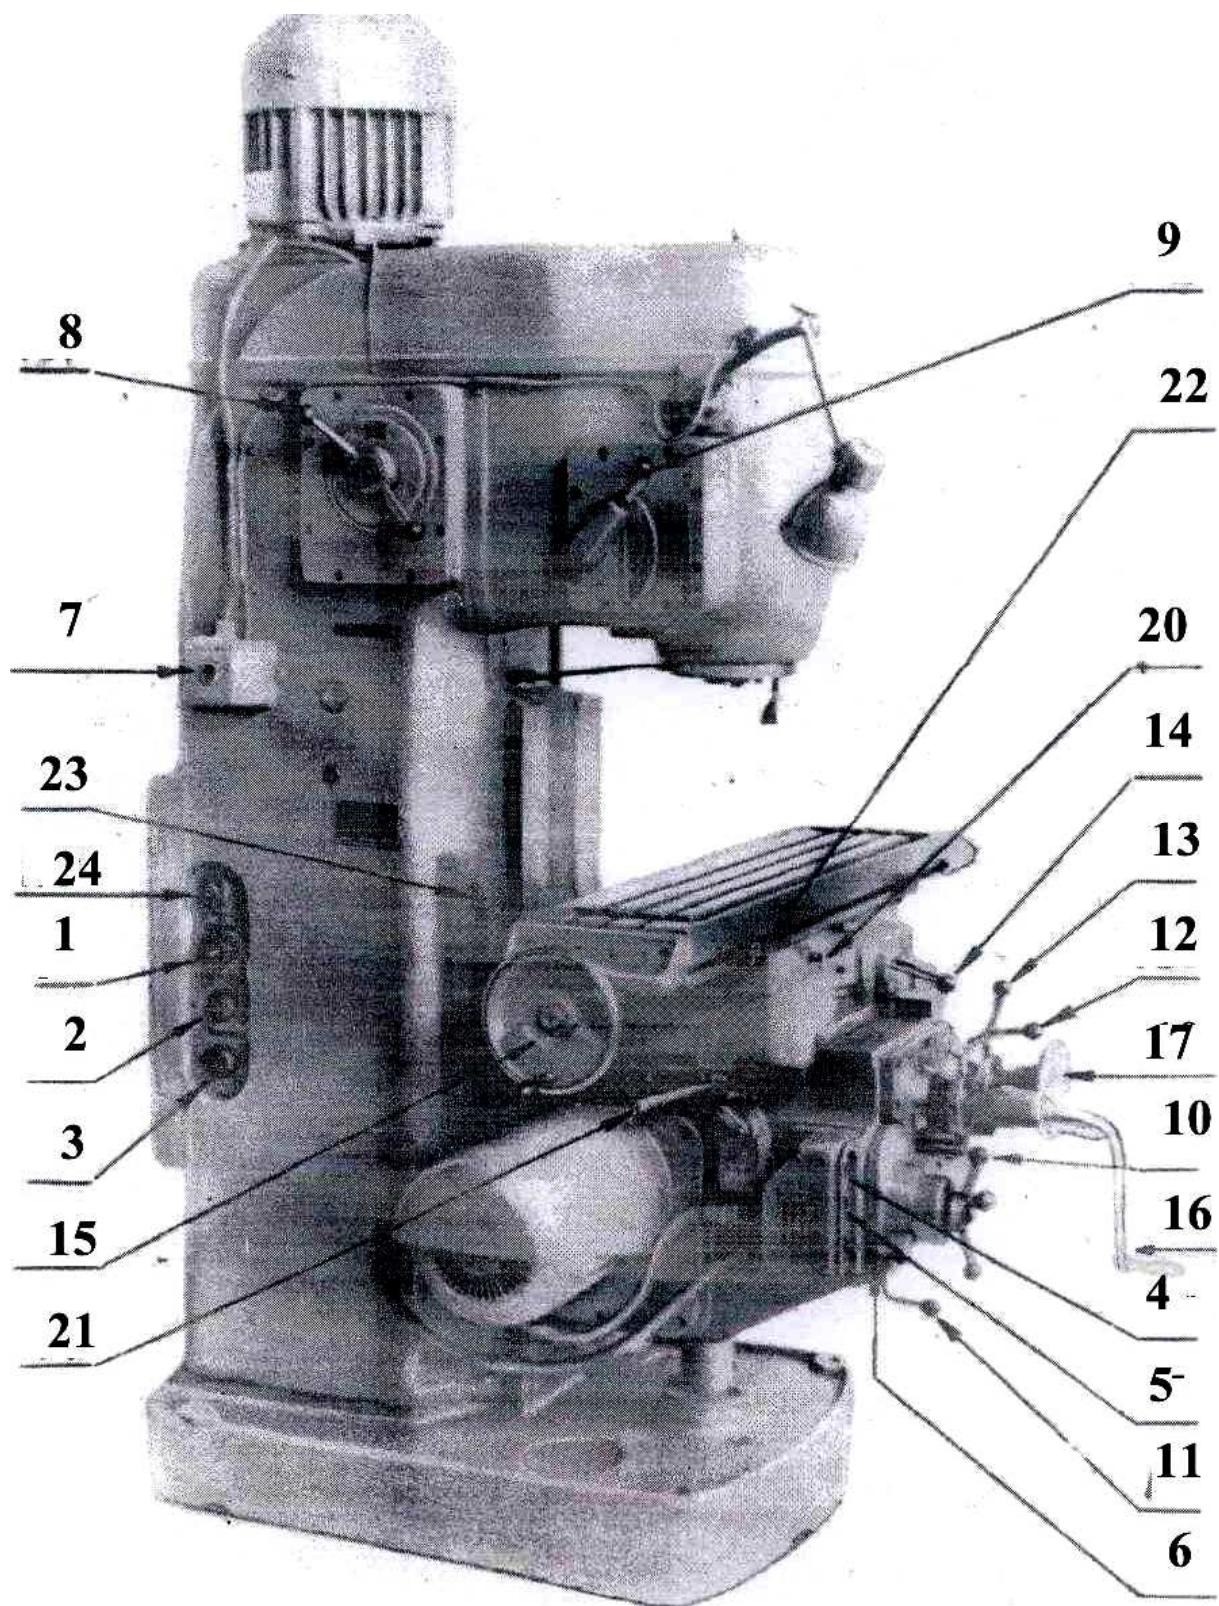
Схема вертикально-фрезерного станка 6Н11.
